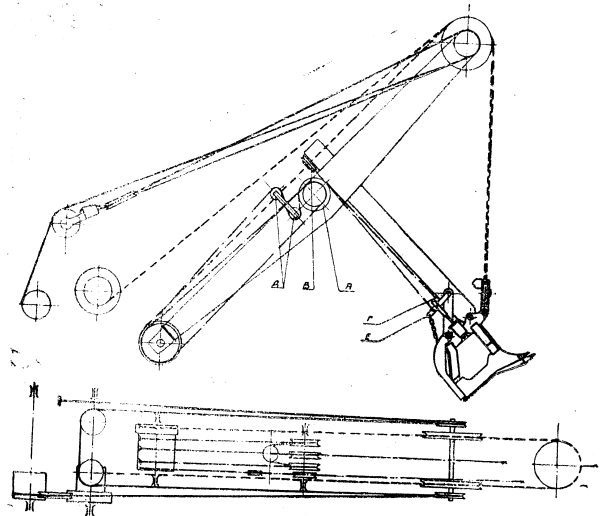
Запасовка канатов при работе прямой лопатой: Д — ролик; В — уравнительный блок; А — блок; Г — коуш; Е — рычаг
